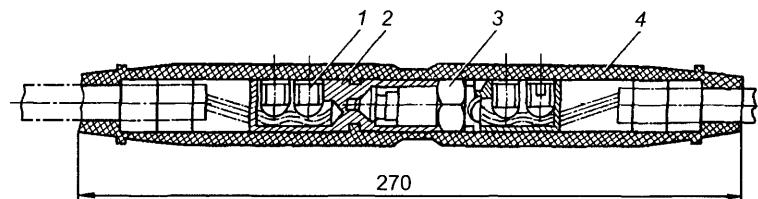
Быстроразъемная муфта МСБ-2:
